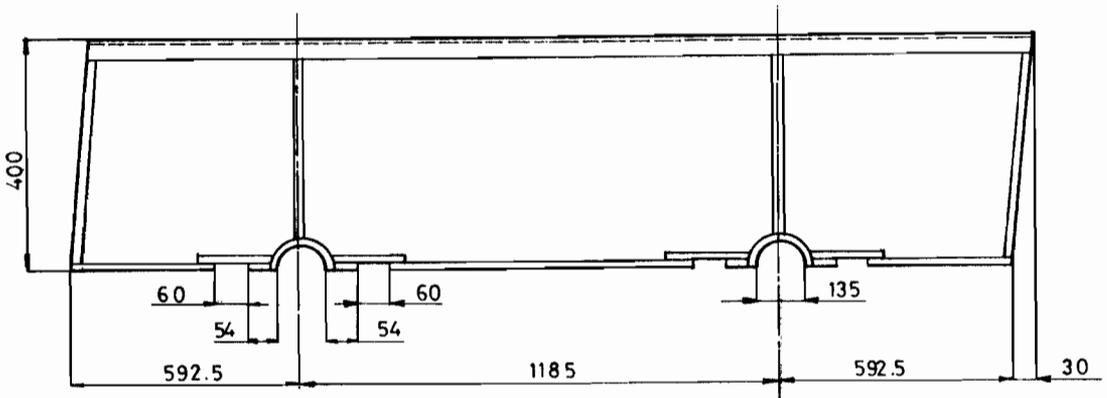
PLANTILLA PARA CORTE DE PLANCHAS DE ARMAZON
